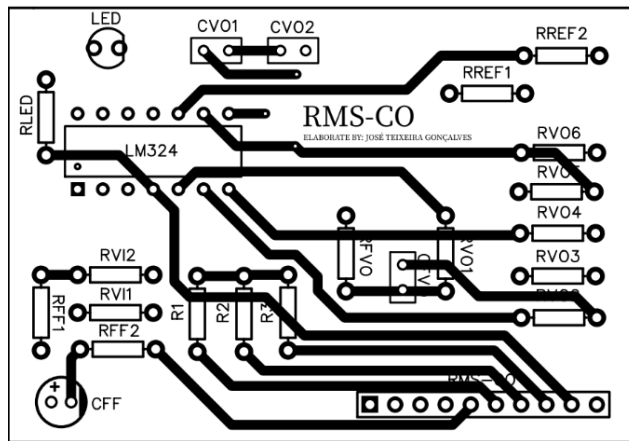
Placa PCB da camada superior do circuito V_{ff} e V_o .
